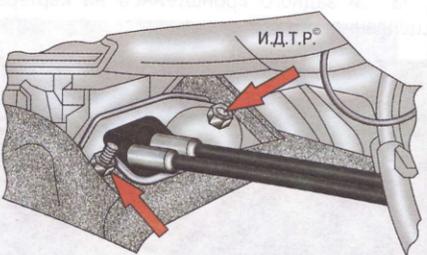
Крепление уплотнителя тросов управления коробкой передач
